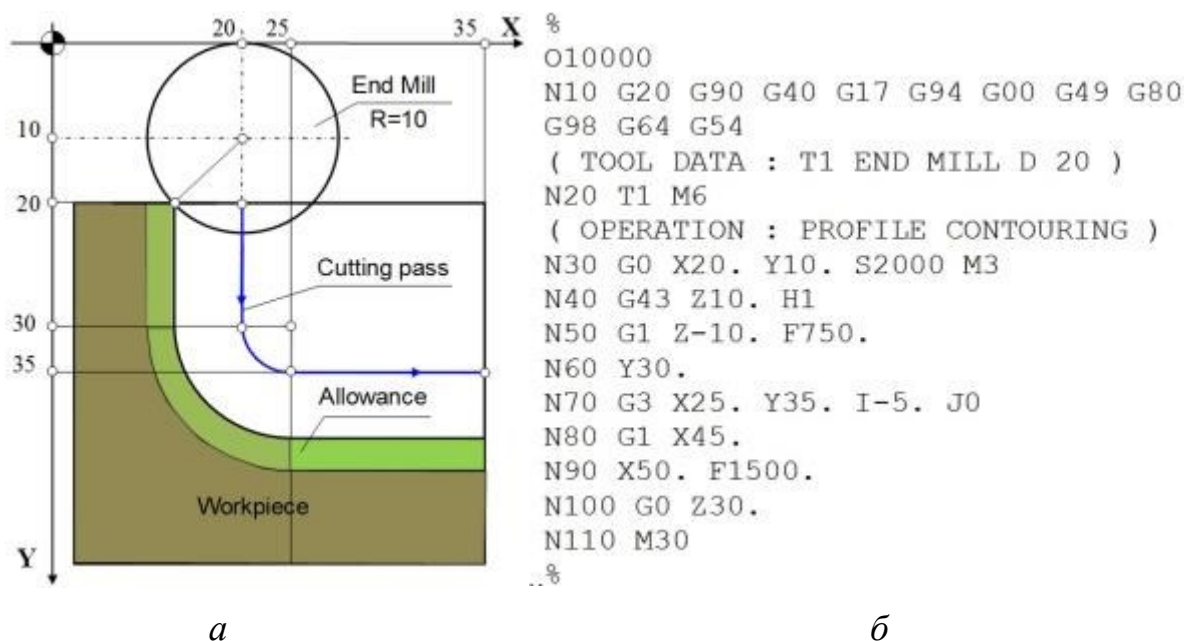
Контур деталі для фрезерування: *а* – розрахункова схема;
